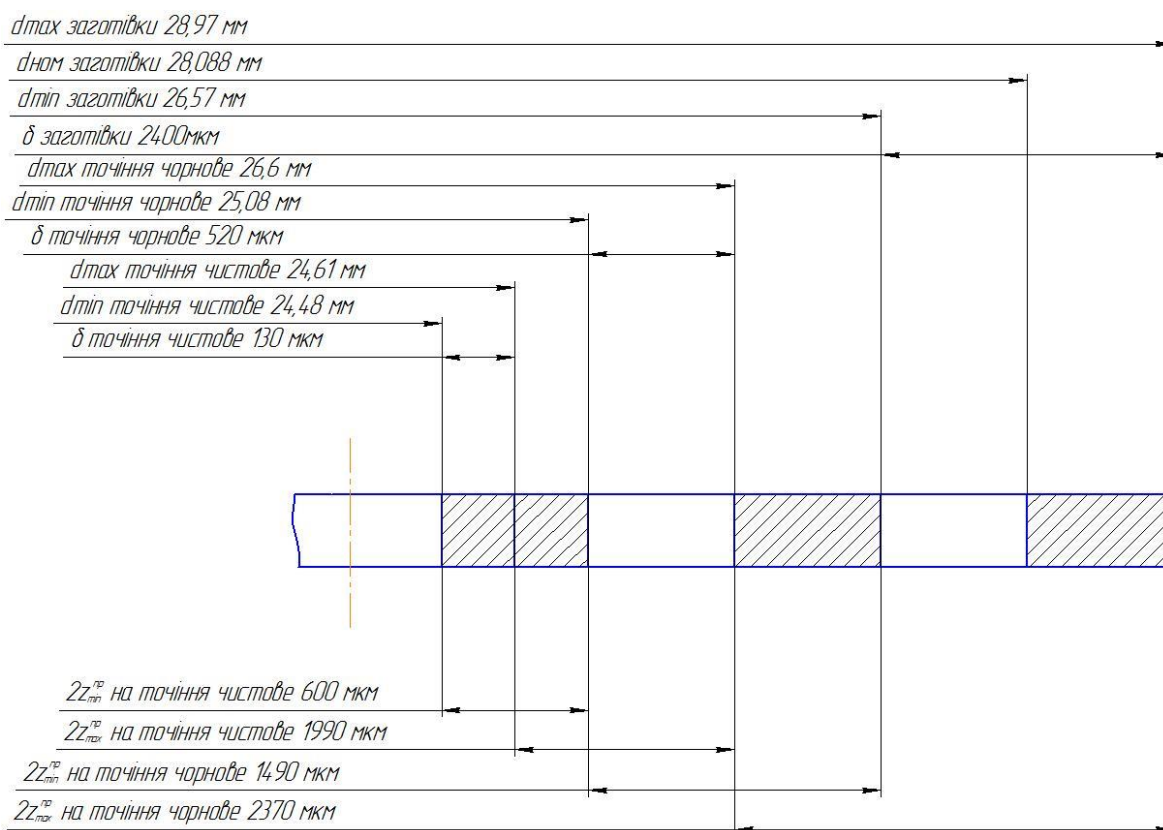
Схема графічного розташування припусків і допусків на обробку зовнішньої поверхні
